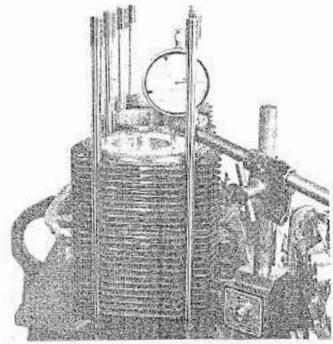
Contrôle de la distance entre la tête du piston et le plan d'appui de la culasse
